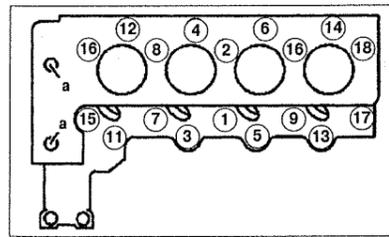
Порядок затяжки болтов крепления головки блока цилиндров
